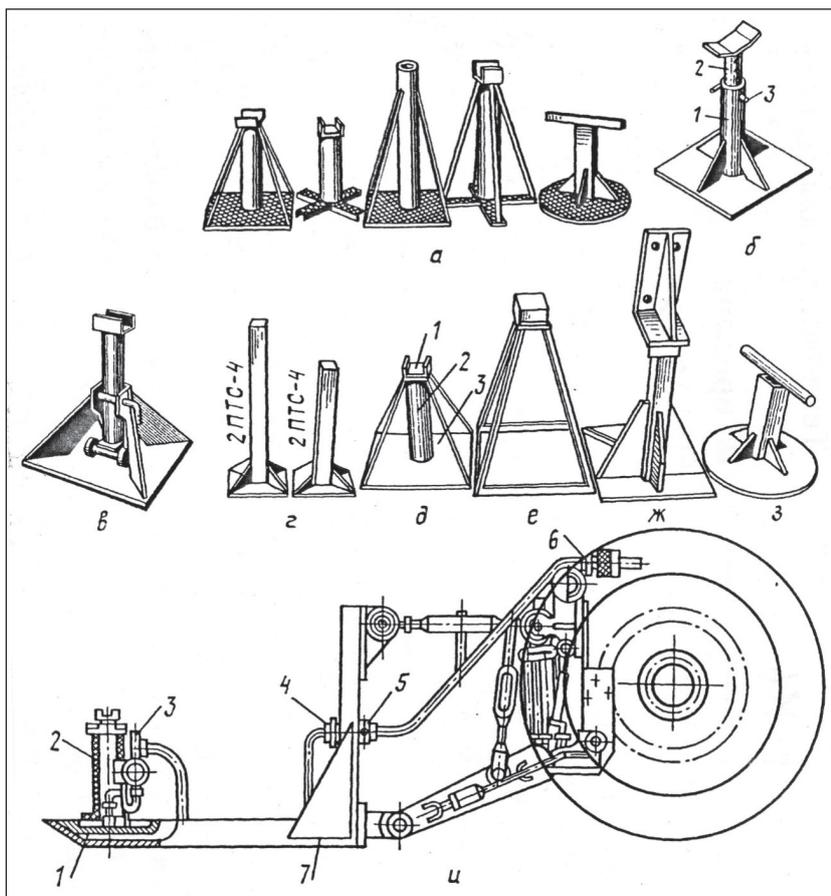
Подставки под машины: 1 – стойка сварная; 2 – стойка передвижная; 3 – штифт; а – подставки из отходов и деталей списанных машин; в – подставка унифицированная ППС-87; г – маркировка подставок по их назначению; б – подставка, регулируемая по высоте;
